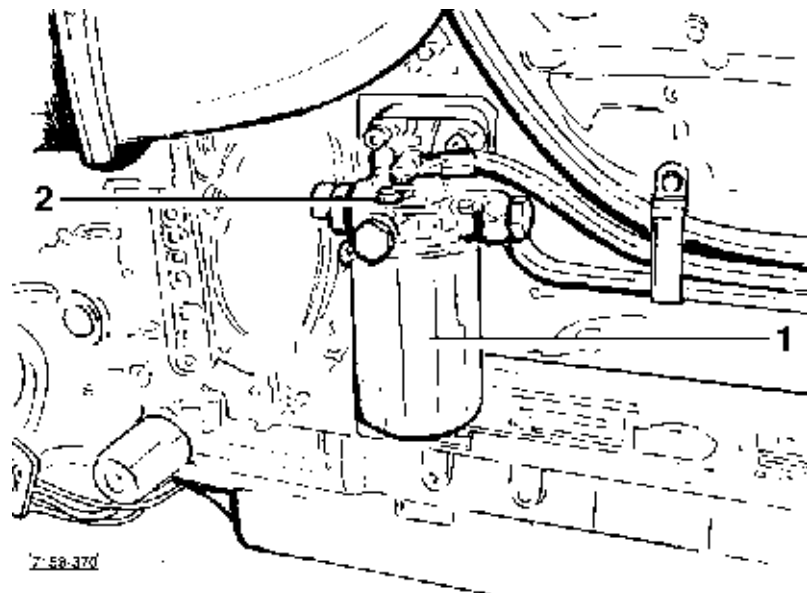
Filtres de carburant - (4 CYLINDRES)
